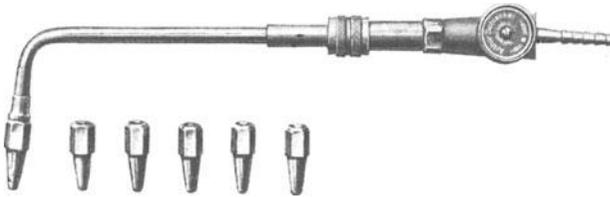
Wasserstoffschweißbrenner in Ansicht.
